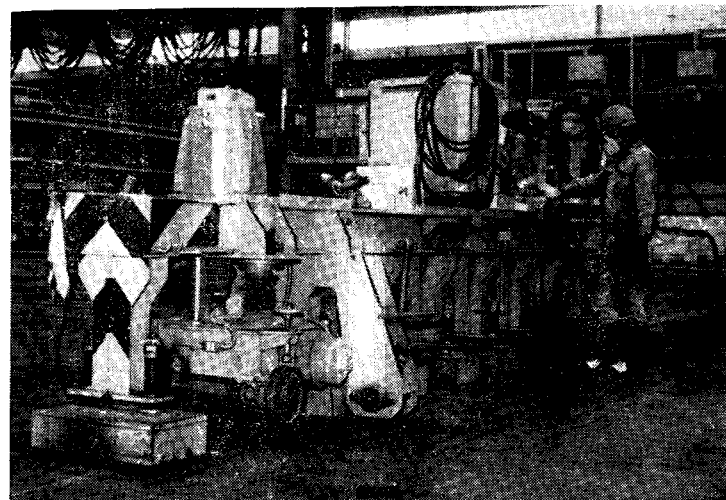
Автоматическая сварочная машина для центровки и прихватки швов горизонтальных полотнищ.
